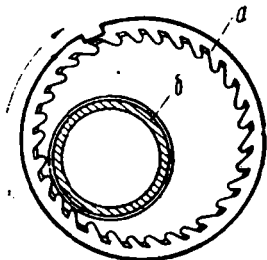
Разрез резьбовой фрезы со вставными зубьями.
